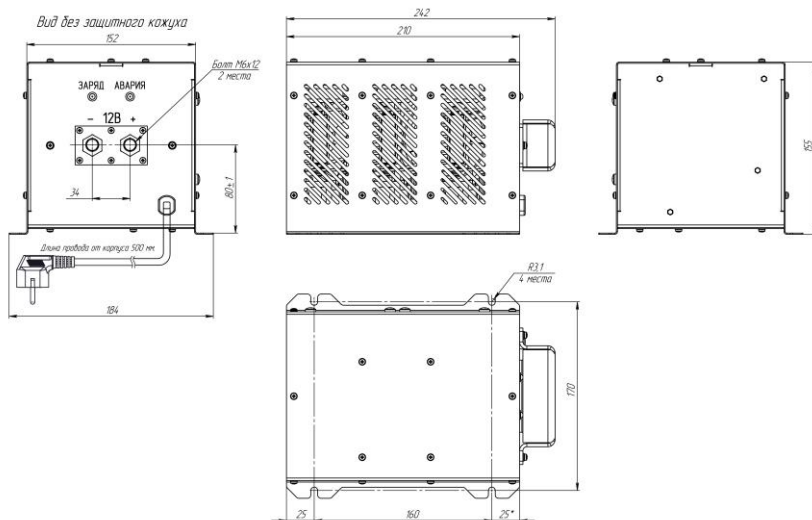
Внешний вид зарядного устройства ЗУ1-12-45
